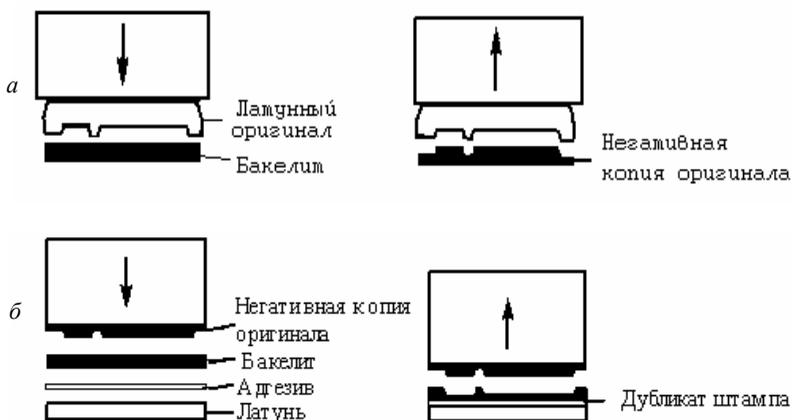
Процесс изготовления бакелитового дубликата: *а* — изготовление негативной копии оригинала; *б* — изготовление дубликата штампа
